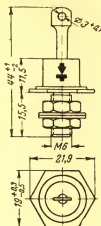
Габаритный чертеж диодов Д302—Д305.
